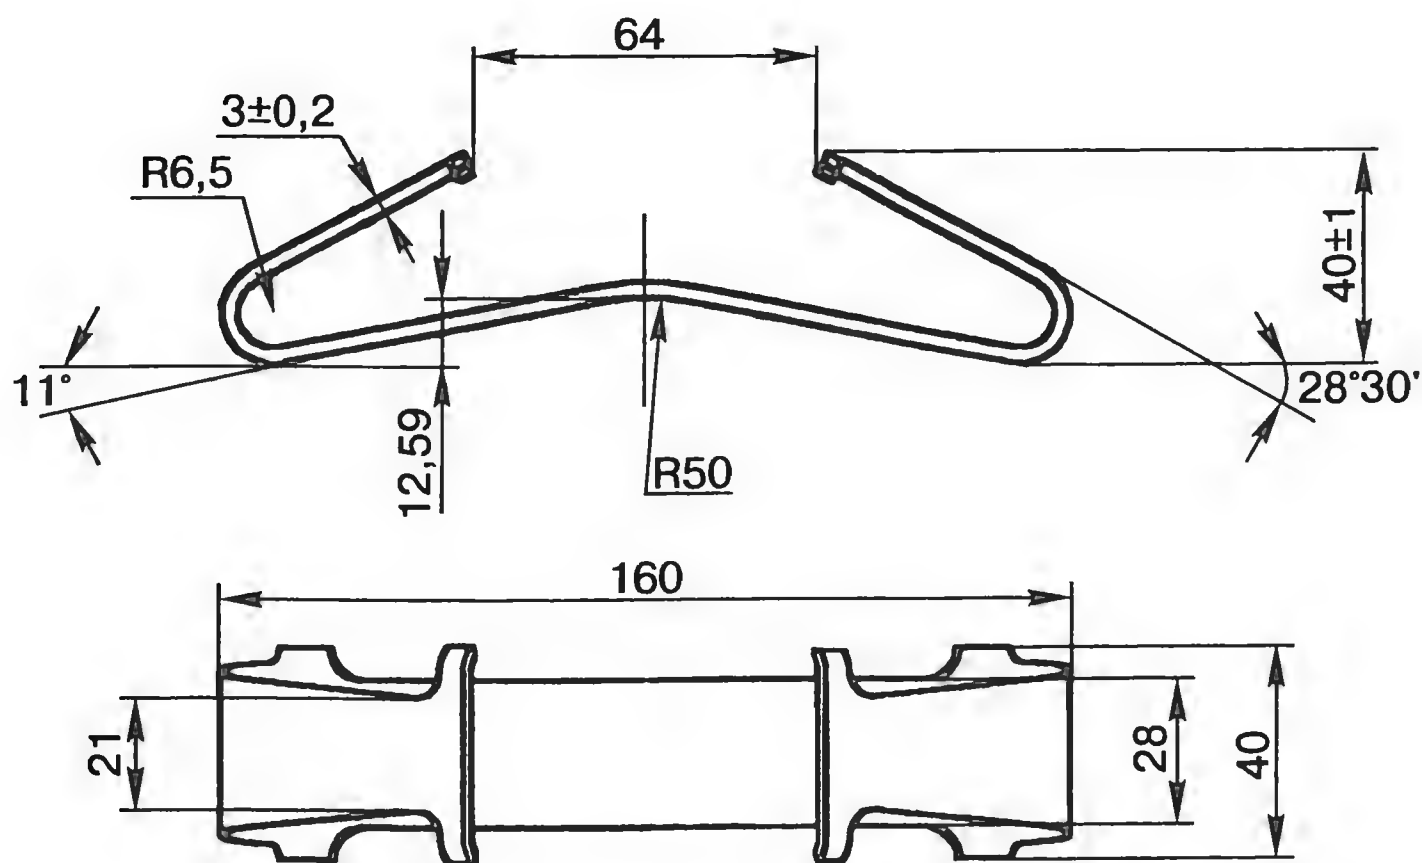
Соединитель рельсовый пружинного типа РП-2М
